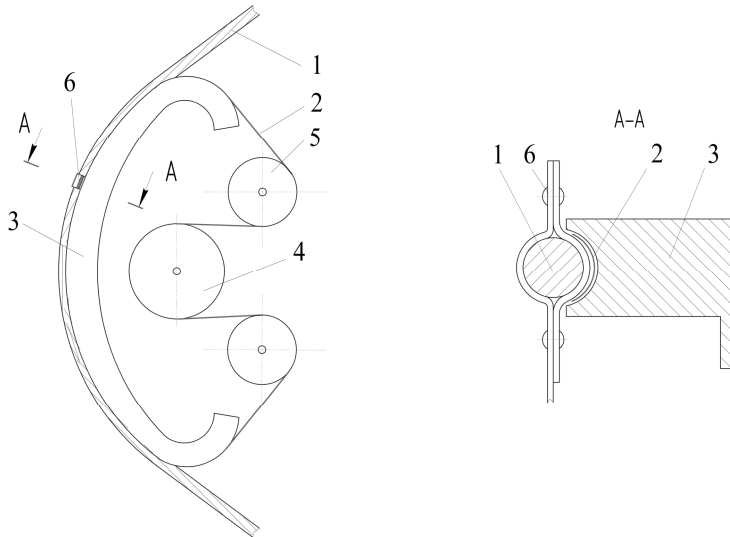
Схема ременного привода тягового каната (вид сверху и разрез): 1 – тяговый канат, 2 – ремень, 3 – неподвижная направляющая, 4 – приводной шкив, 5 – отклоняющие шкивы, 6 – подвеска
